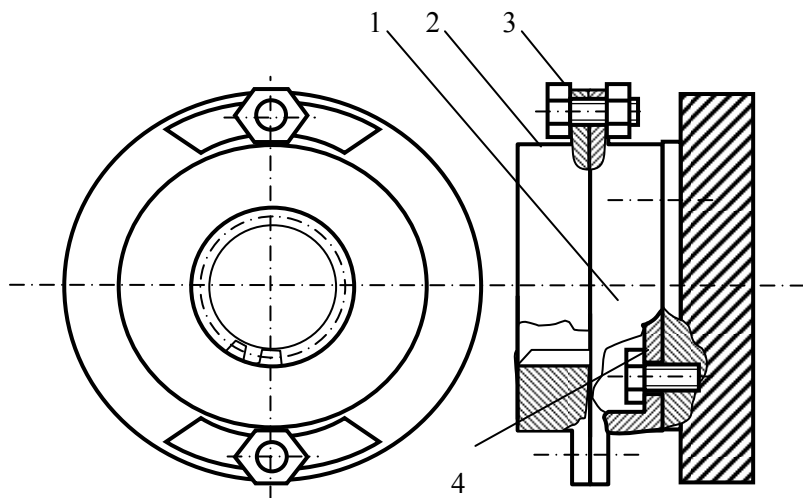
Муфта бесступенчатого изменения угла начала подачи и впрыска топлива
